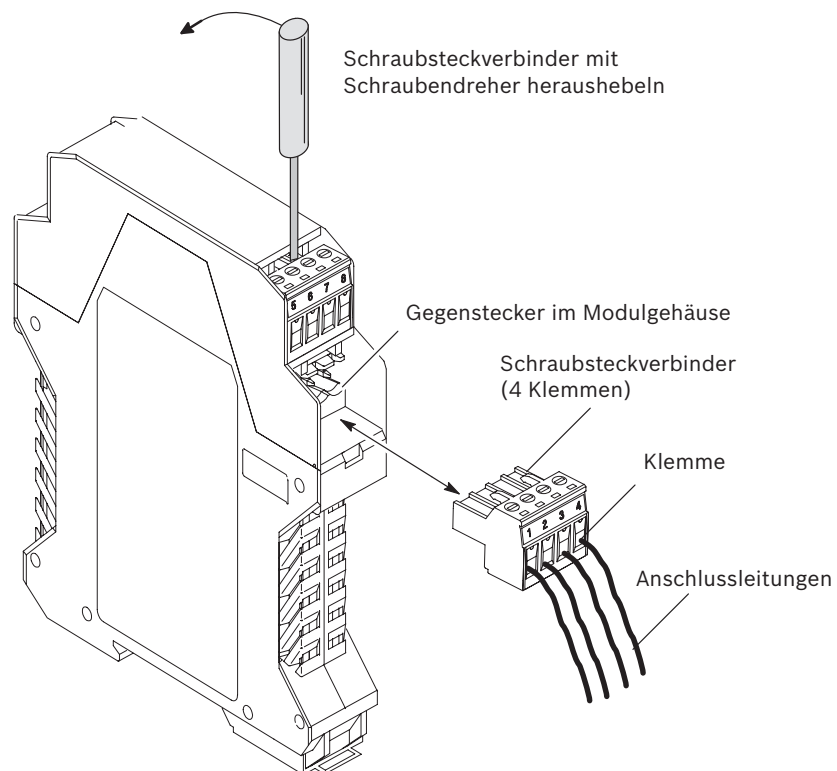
Klemmanschlüsse der Schraubsteckverbinder
